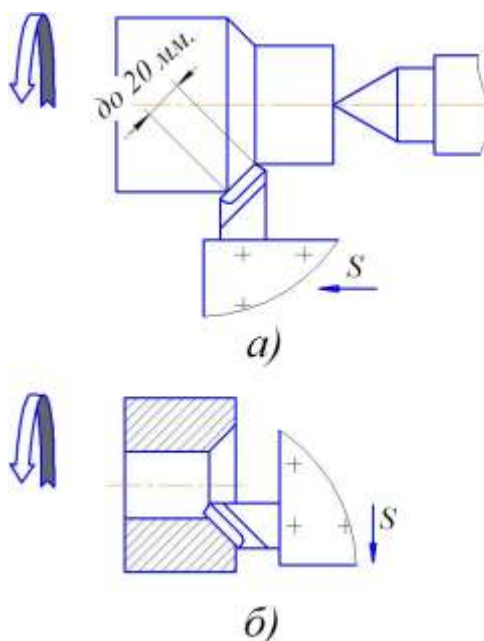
Обработка коротких конических поверхностей широким резцом: а) наружные поверхности; б) внутренние поверхности
